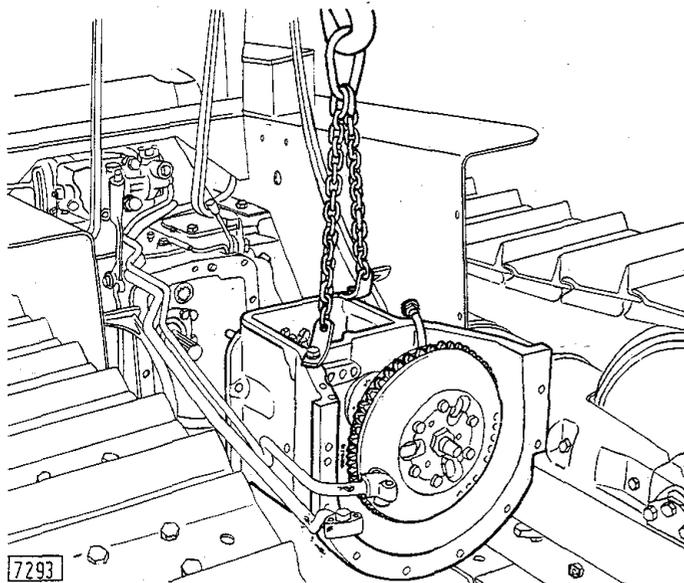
Stacco (riattacco) del gruppo motore-sospensione anteriore mediante la catena di sollevamento 290740.
